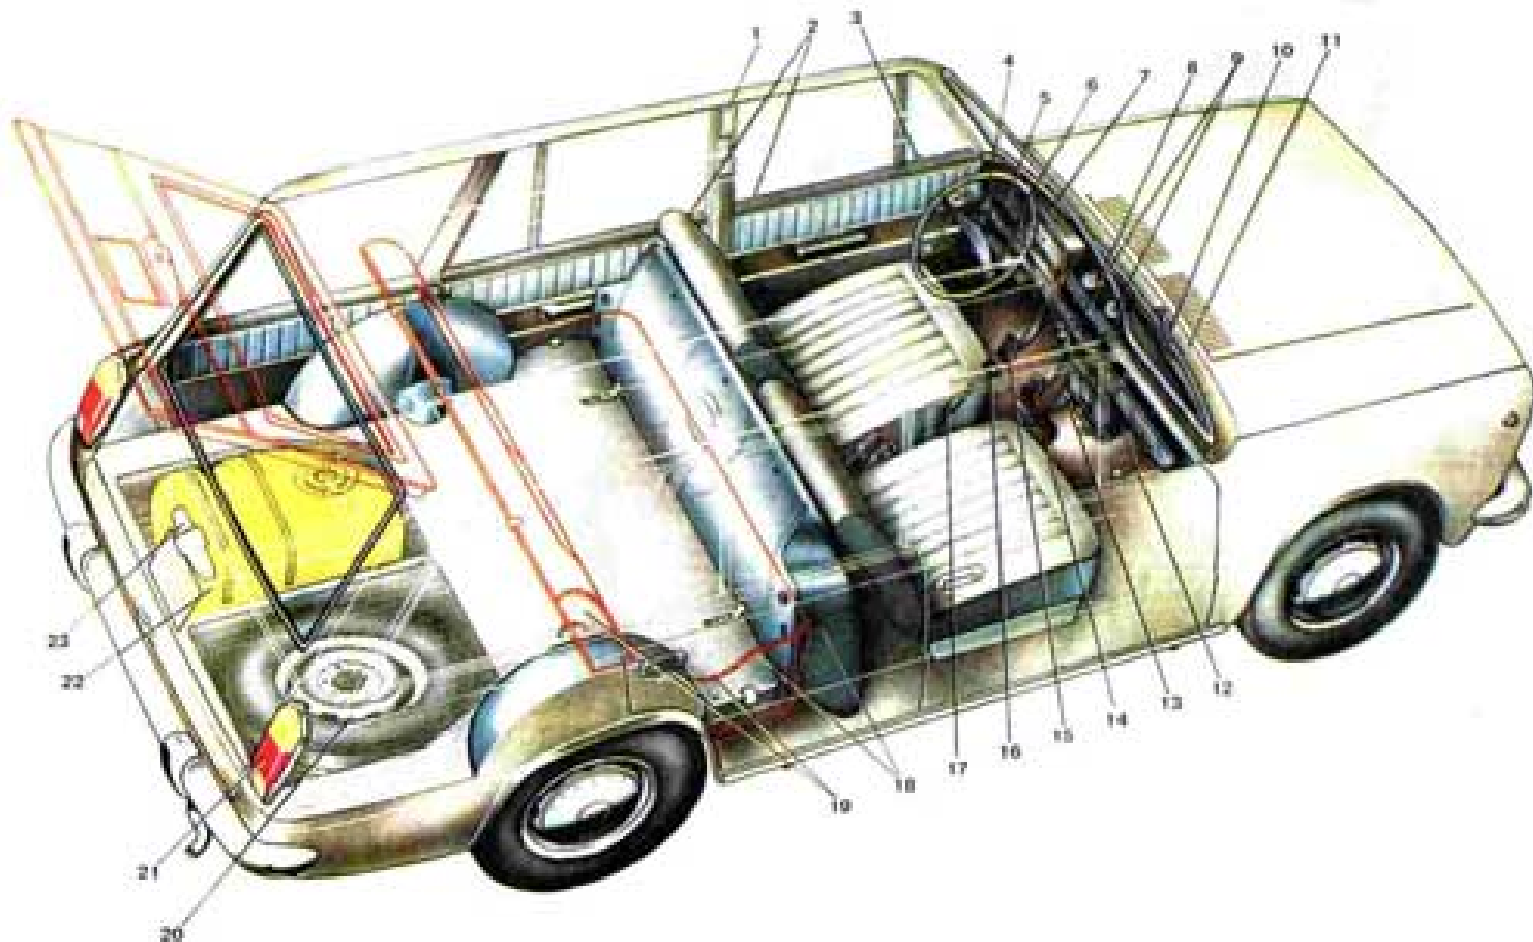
Устройство автомобиля ВАЗ - 2102.1. 1. Плафон; 2. Кнопки блокировки замков дверей; 3. Рычаг запора поворотного стекла; 4. Насос смывателя ветрового стекла; 5. Блок выключателей; 6. Рулевое колесо; 7. Щиток приборов; 8. Рычаги управления отоплением и вентиляцией; 9. Дефлекторы обогрева ветрового стекла; 10. Стеклоочиститель; 11. Жиклер стеклосмывателя; 12. Отопитель; 13. Педаль привода дроссельных заслонок; 14. Педаль тормоза; 15. Педаль сцепления; 16. Рычаг переключения передач; 17. Рычаг ручного тормоза; 18. Заднее сиденье в откинутом и нормальном положениях; 19. Спинка заднего сиде-
